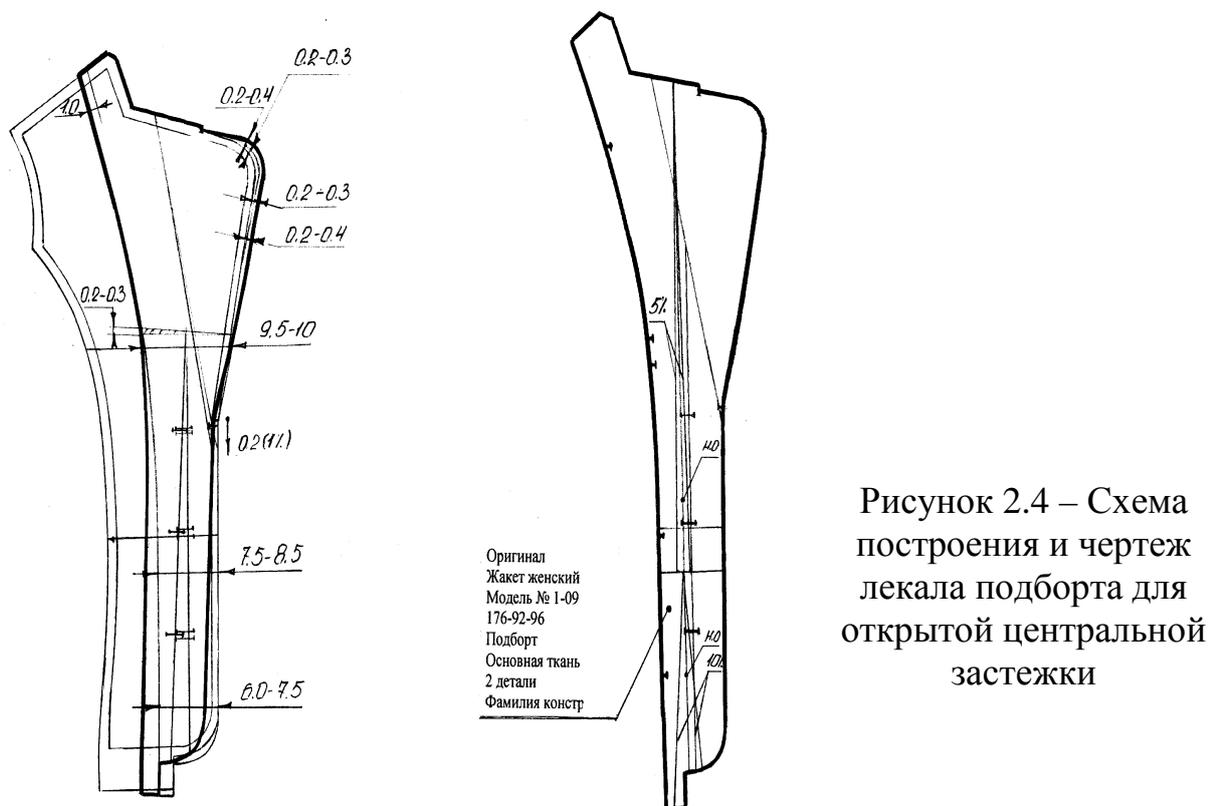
Схема построения и чертеж лекала подборта для открытой центральной застежки
